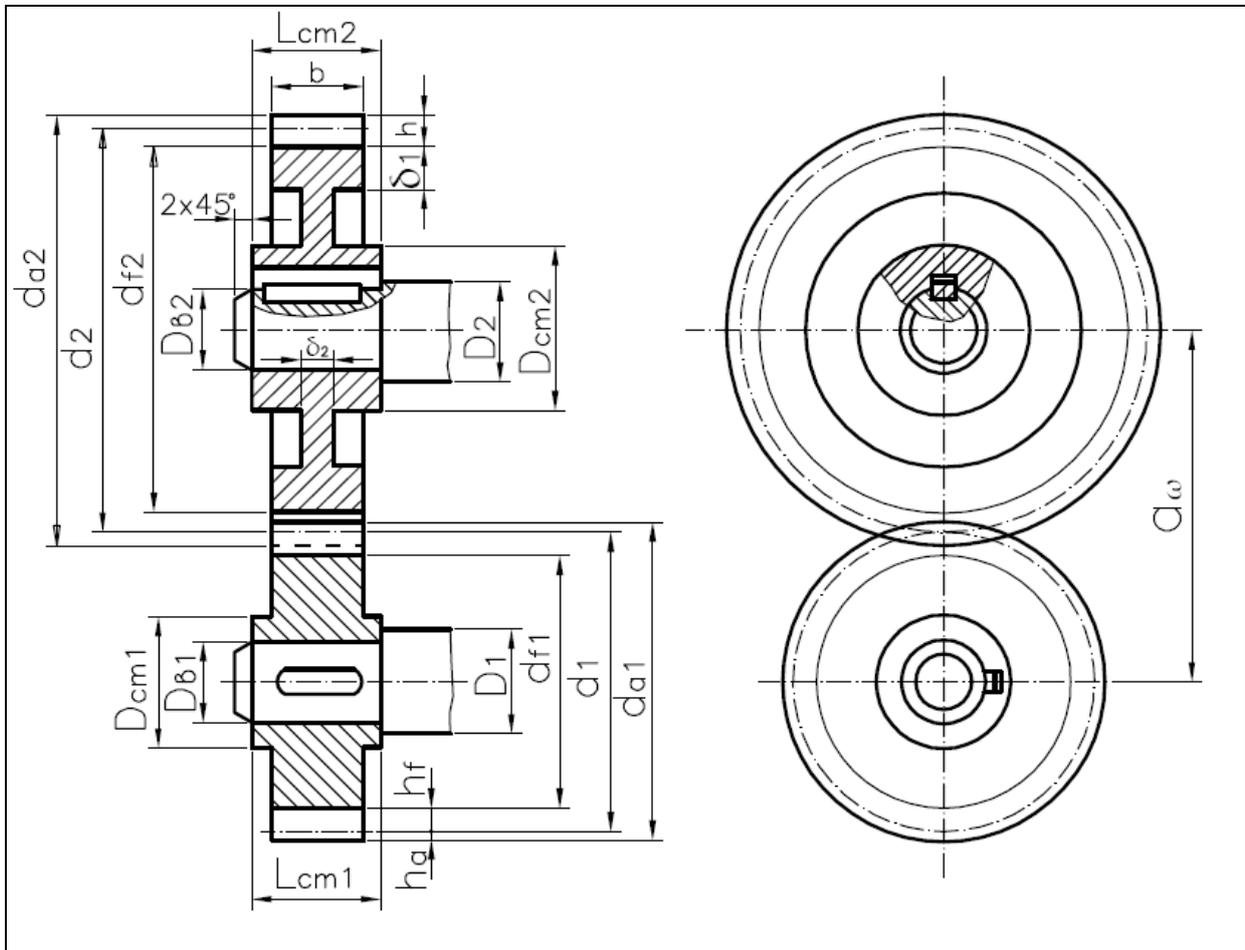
Геометрические параметры цилиндрической зубчатой передачи.
